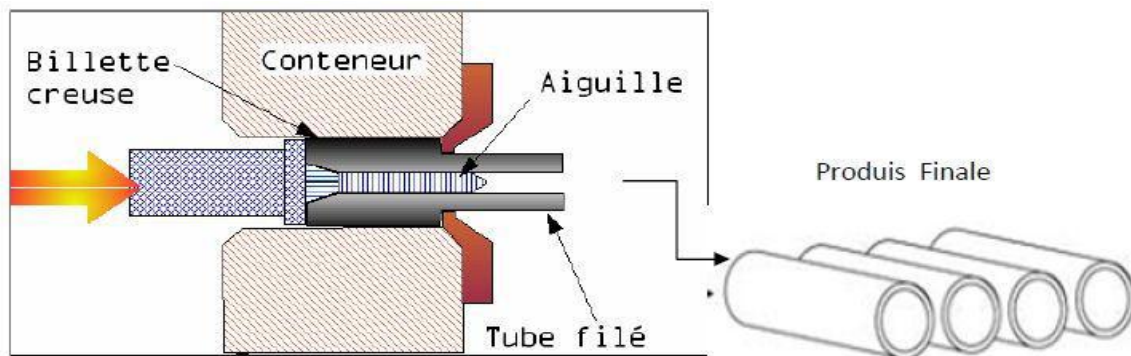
Obtention des tubes sans soudure [HAD 13]
